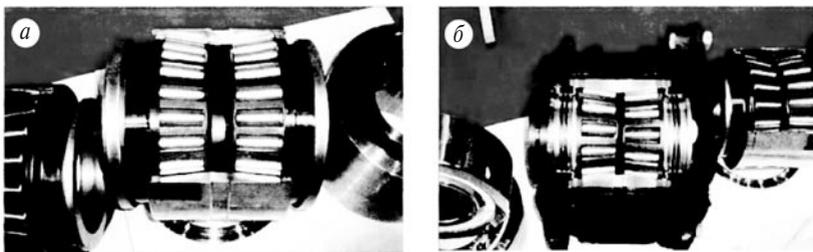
Общий вид деталей конических подшипников кассетного типа для грузовых вагонов:
